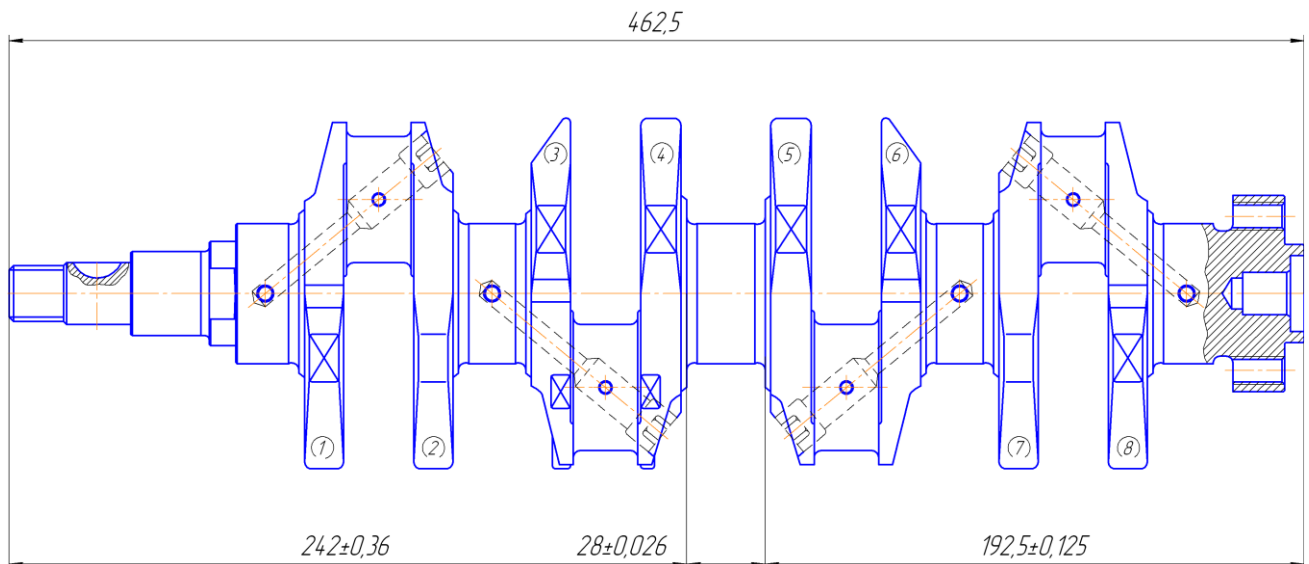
Схема деталі для визначення розмірного ланцюга
